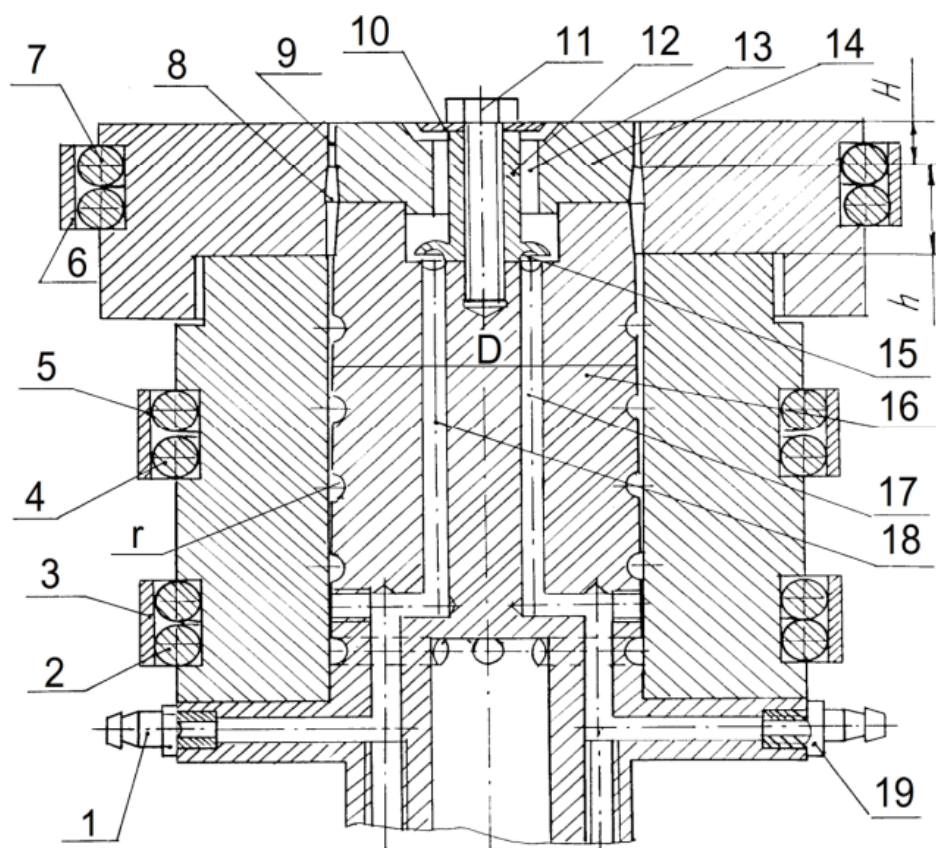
Екструзійна головка для виготовлення рукавної полімерної плівки
